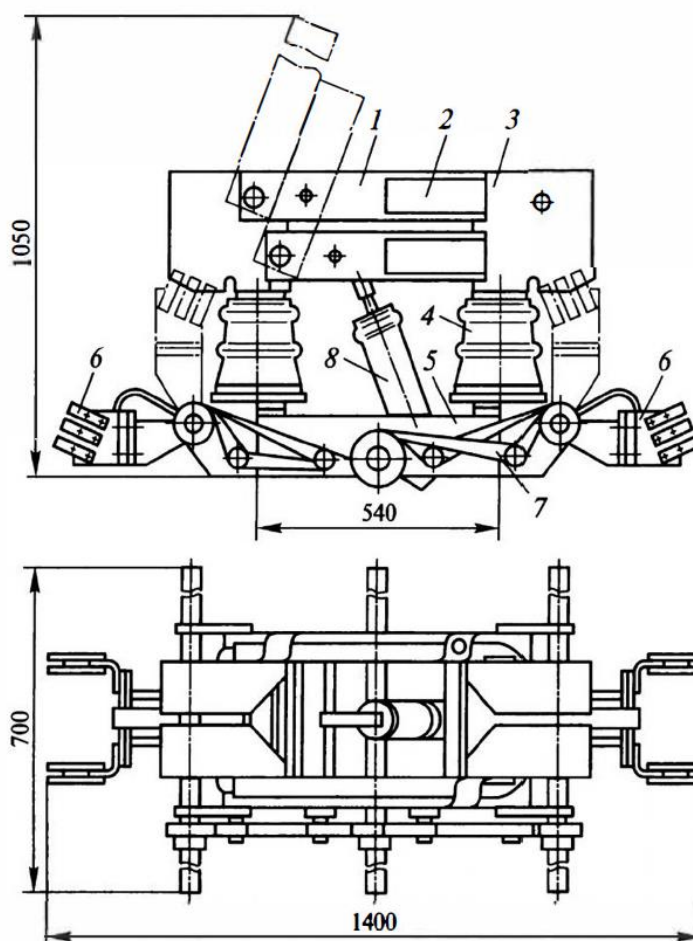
Разъединитель рубящего типа для внутренней установки с двумя заземляющими ножами РВРЗ-2-20/8000 (один полюс):
